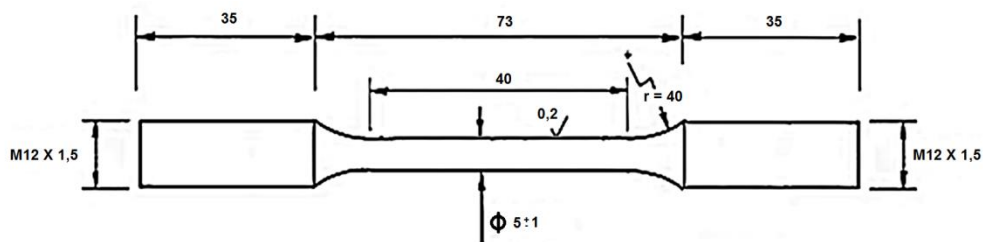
Dimensões em milímetros dos corpos de prova para os ensaios de tração do metal base e das juntas soldadas de trilhos ferroviários. Seção circular e cabeças com rosca.
